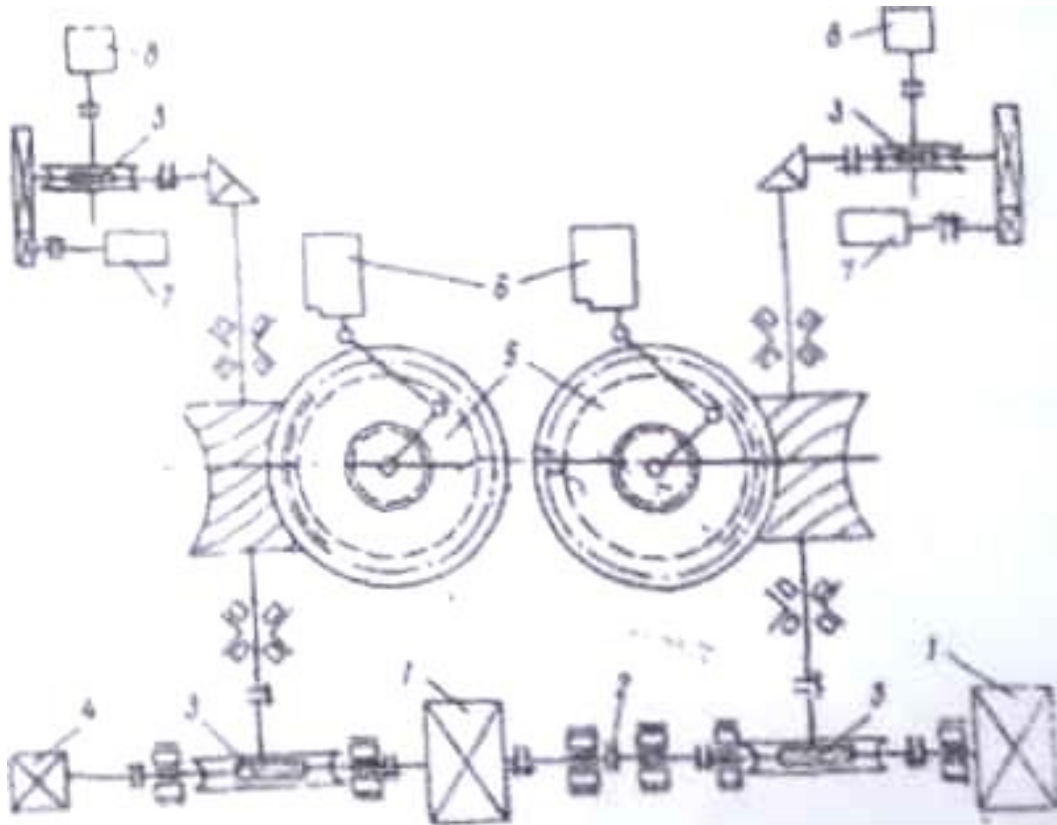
Кінематична схема НМ електромеханічного типу кліті кварто 600/1500x1700 стана холодної прокатки: 1 - електродвигун, 2 — електромагнітна муфта; 3 - черв'ячний редуктор; 4 - тахогенератор. 5 — глобоїдний редуктор, б - датчик кута повороту гвинта; 7 - сельсин-датчик ,8 - командо апарат.
